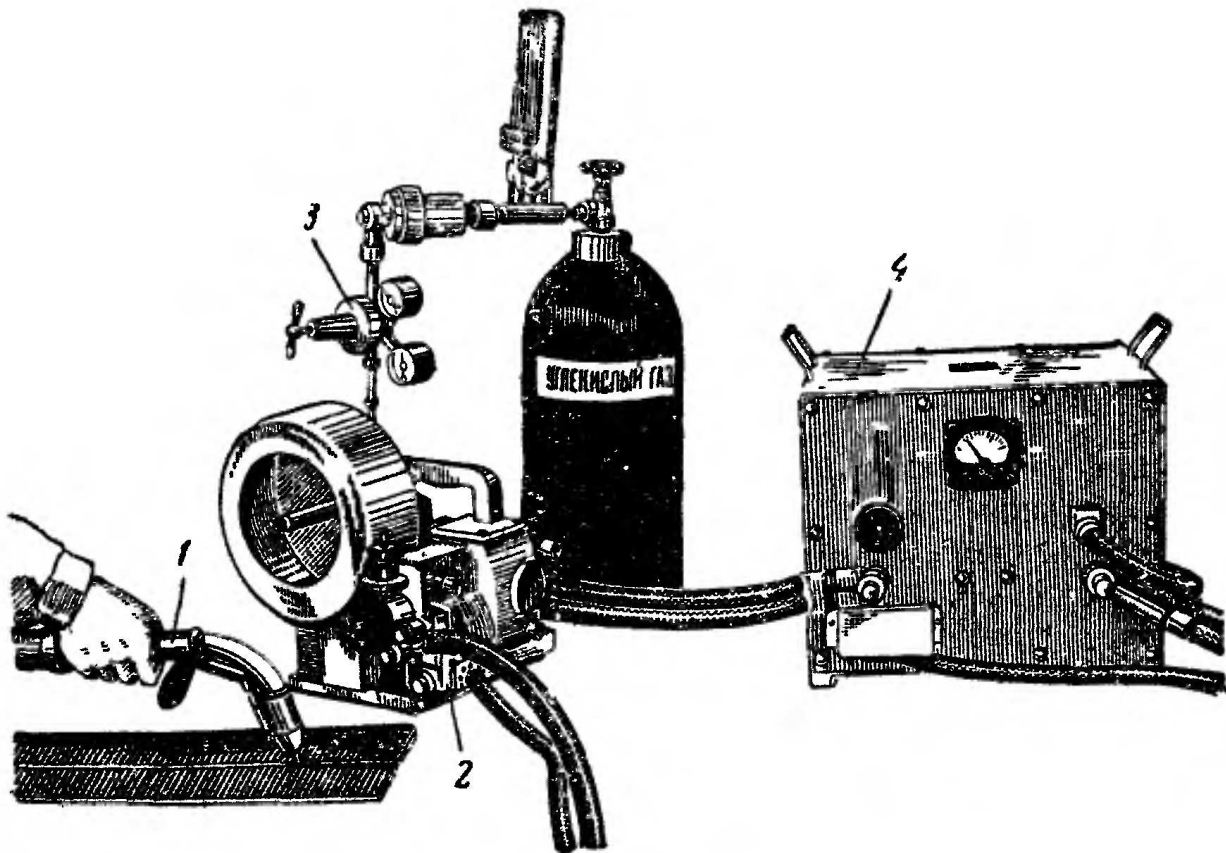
Полуавтомат А-537 для сварки в среде углекислого газа проволокой 1,6—2,0 мм:
